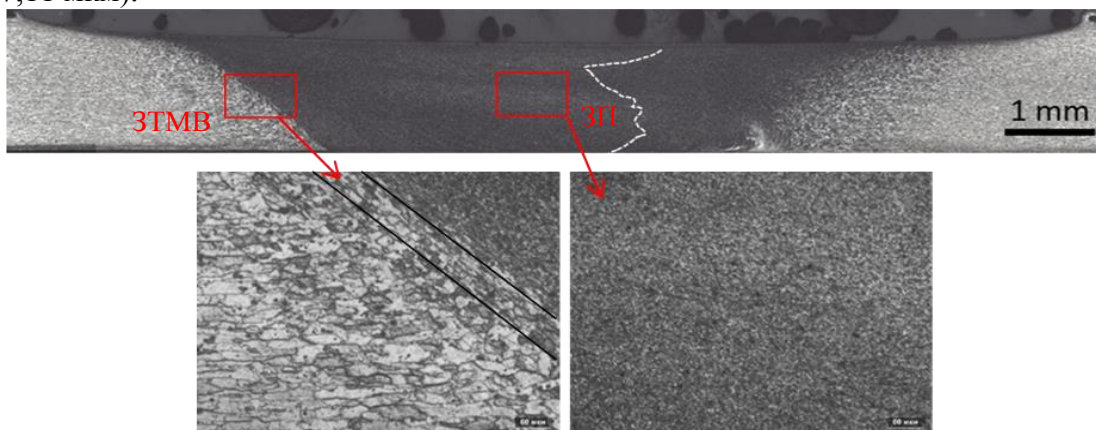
Панорамный вид сварного шва и ЗТМВ, ЗП под оптическим микроскопом
